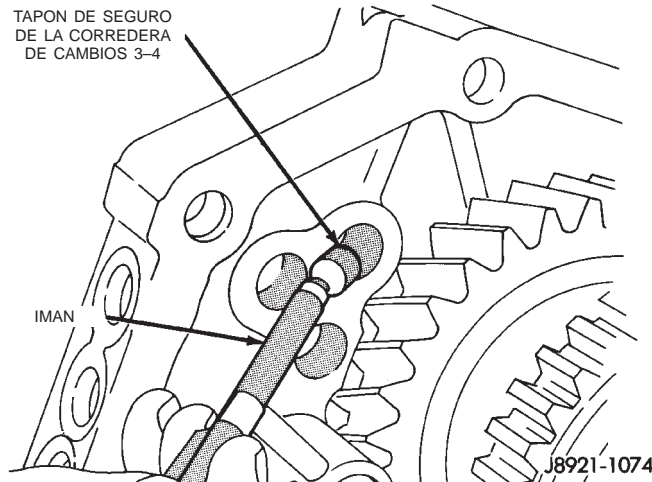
Desmontaje del tapón de seguro de la corredera de cambios 3-4
